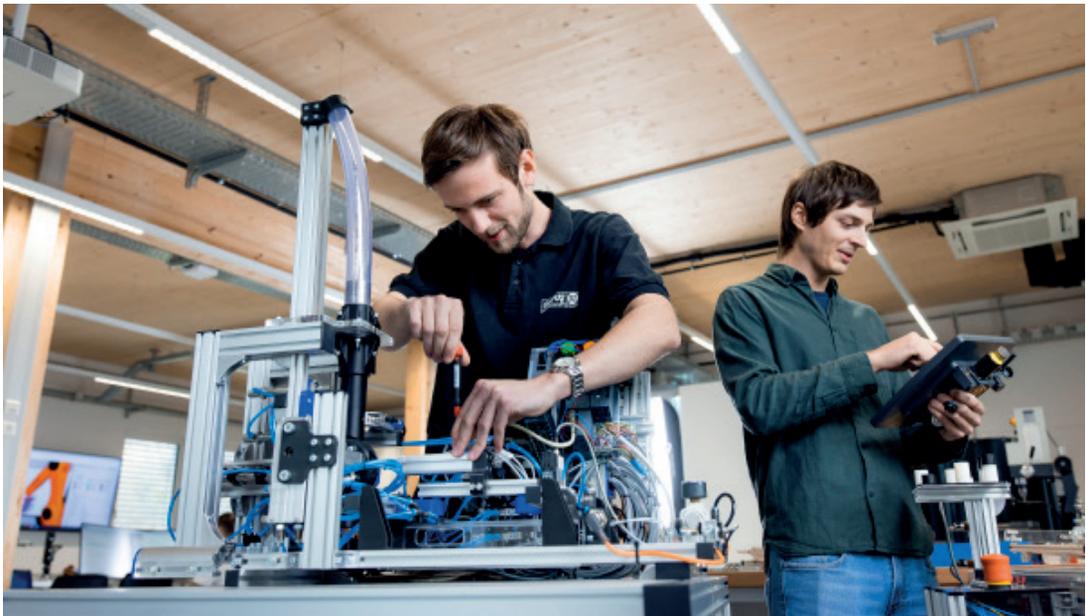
Prototyp-Aufbau einer Richtmaschine für Drahtelemente.
